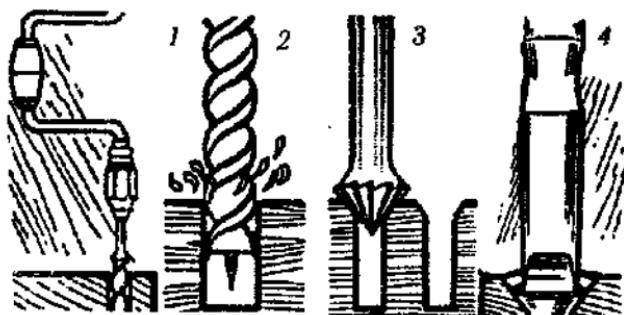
Операции при ввинчивании шурупов: 1, 2 — рассверливание под шурп; 3 — раззенковка; 4 — ввинчивание.
